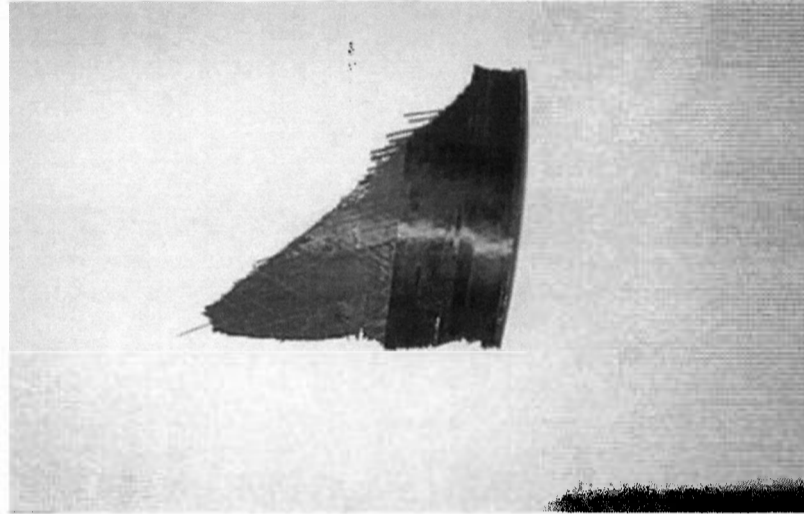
Fragmento de um cilindro, após o ensaio, fabricado pelo método de bobinagem por superposição de camadas.
